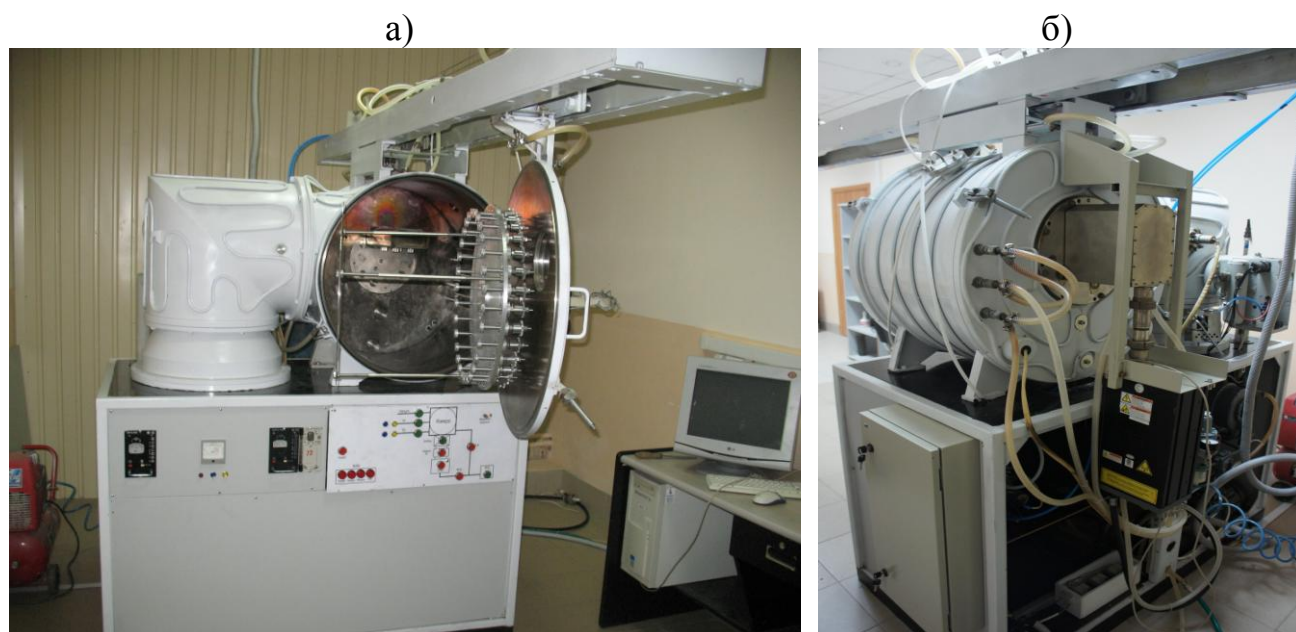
Установка для формирования гибридных покрытий: вид спереди (а), вид сзади (б)
